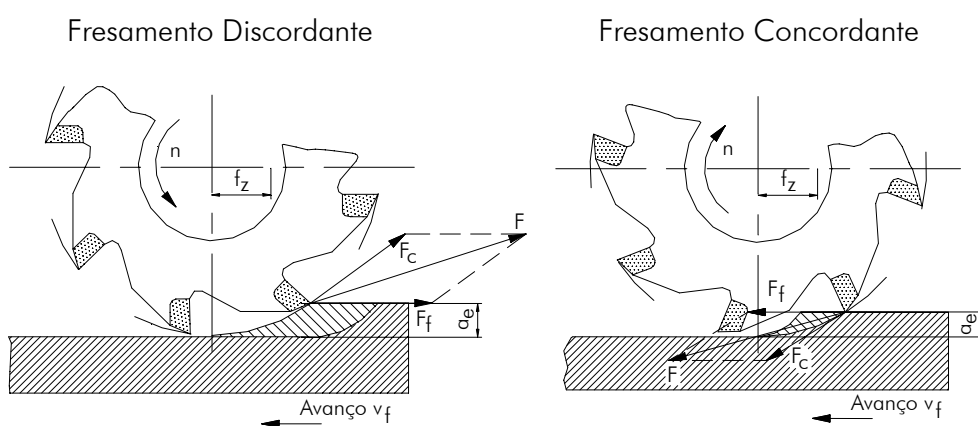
Fresamento periférico concordante e discordante [4]
